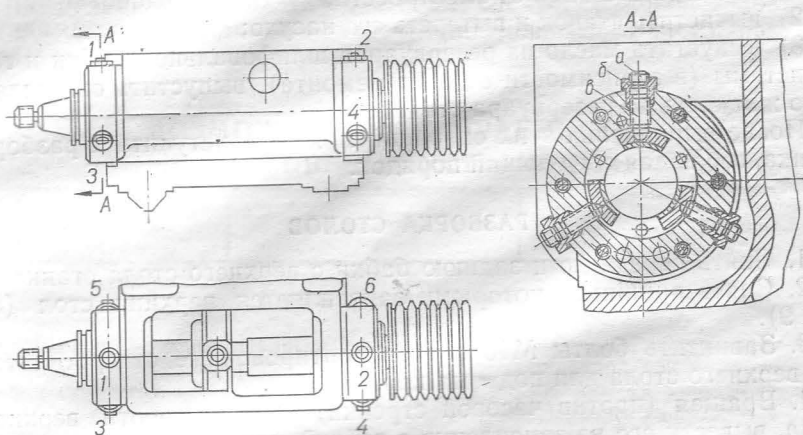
Схема регулирования подшипников шпинделя шлифовальной бабки
